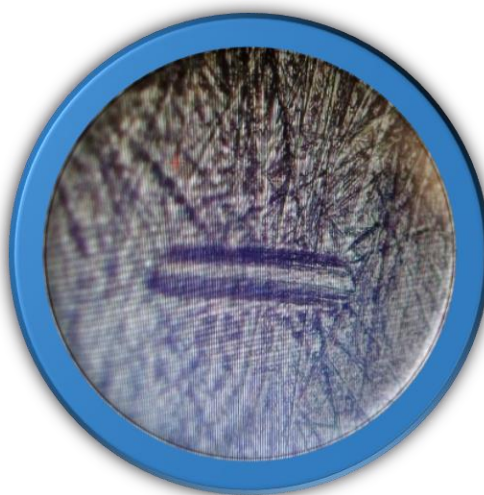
Fotografia de pormenor da chapa nº 425 (1700 quinagens)
